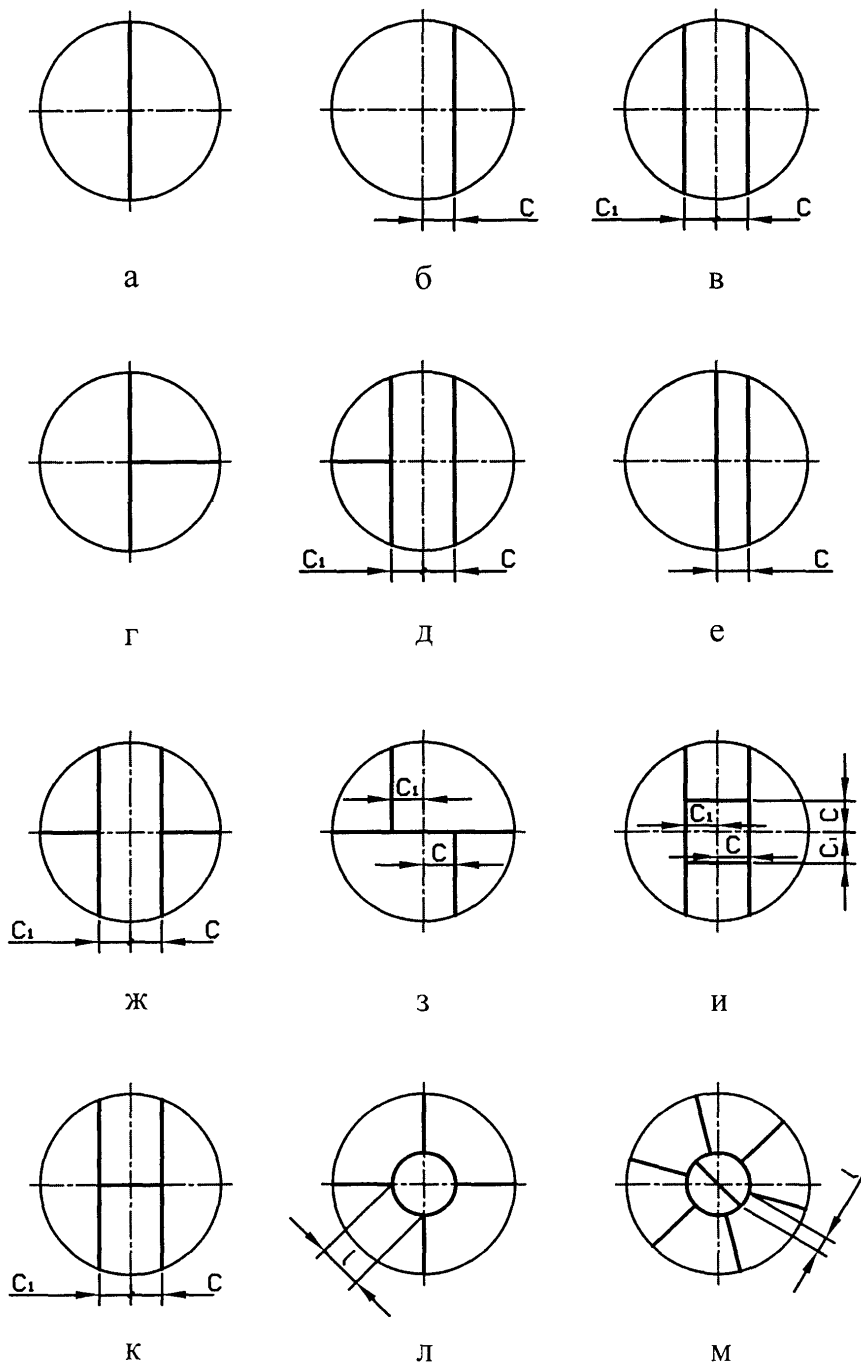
Расположение сварных швов заготовок выпуклых днищ
